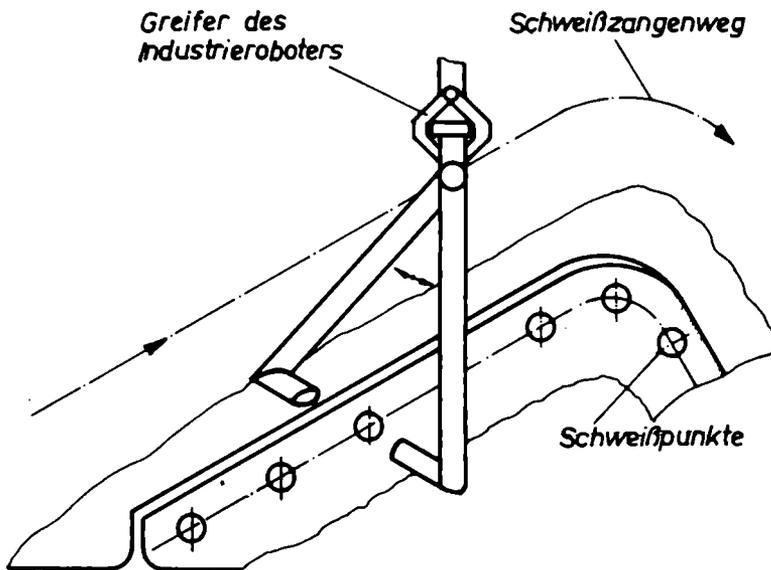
Anfahren der Bahnpunkte beim Punktschweißen
